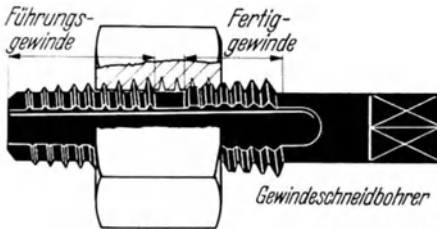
Gewindeschneiden mit Gewindeschneidbohrer. Führung des Gewindeschneidbohrers durch das vorgeschnittene scharfe Führungsgewinde.
